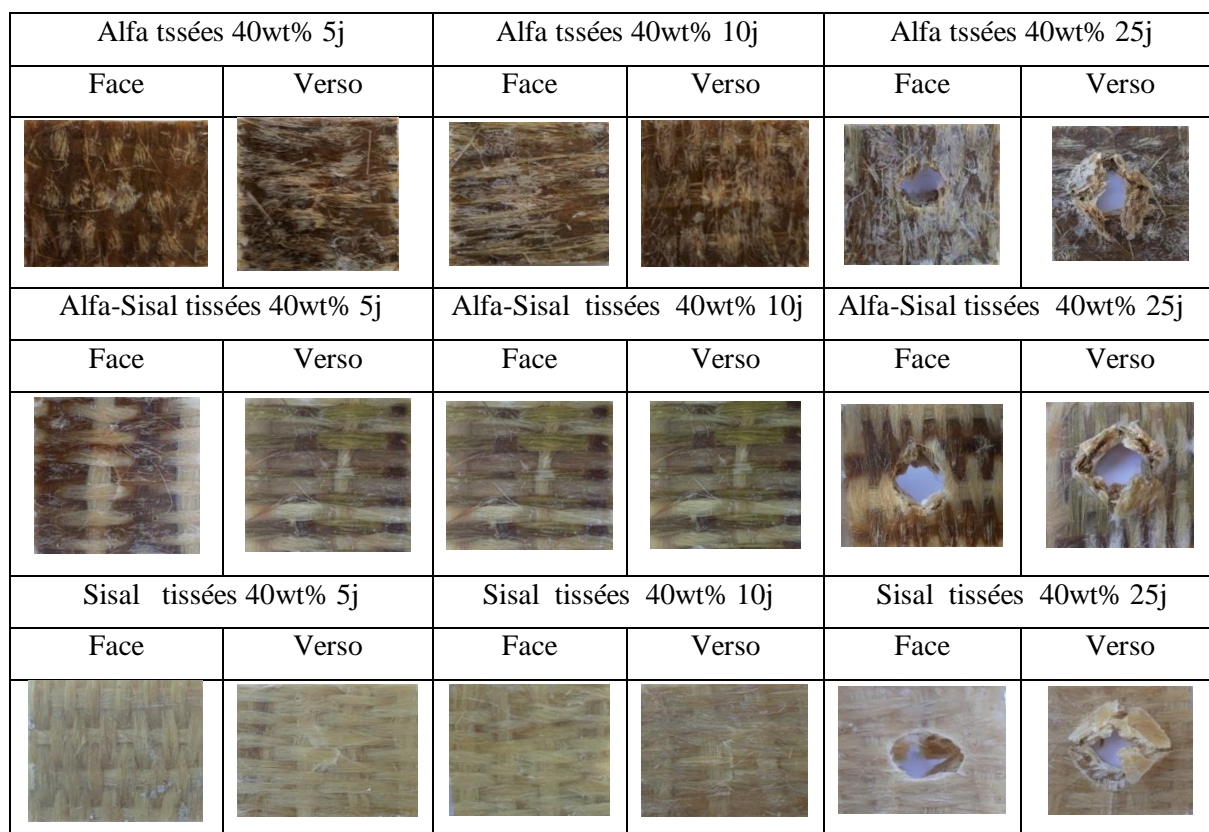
Vues avant et arrière des éprouvettes après essai d'impact.
